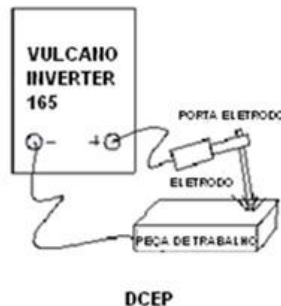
Conexão positiva para soldagem com eletrodo revestido
